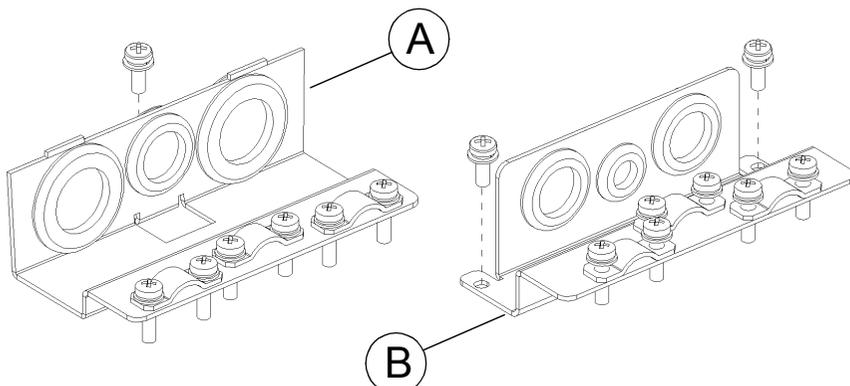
Kabeldurchführungsblech für Leistungskabel (A) und Steuerkabel (B); Frequenzumrichter des Typs IP 21 / NEMA1.
